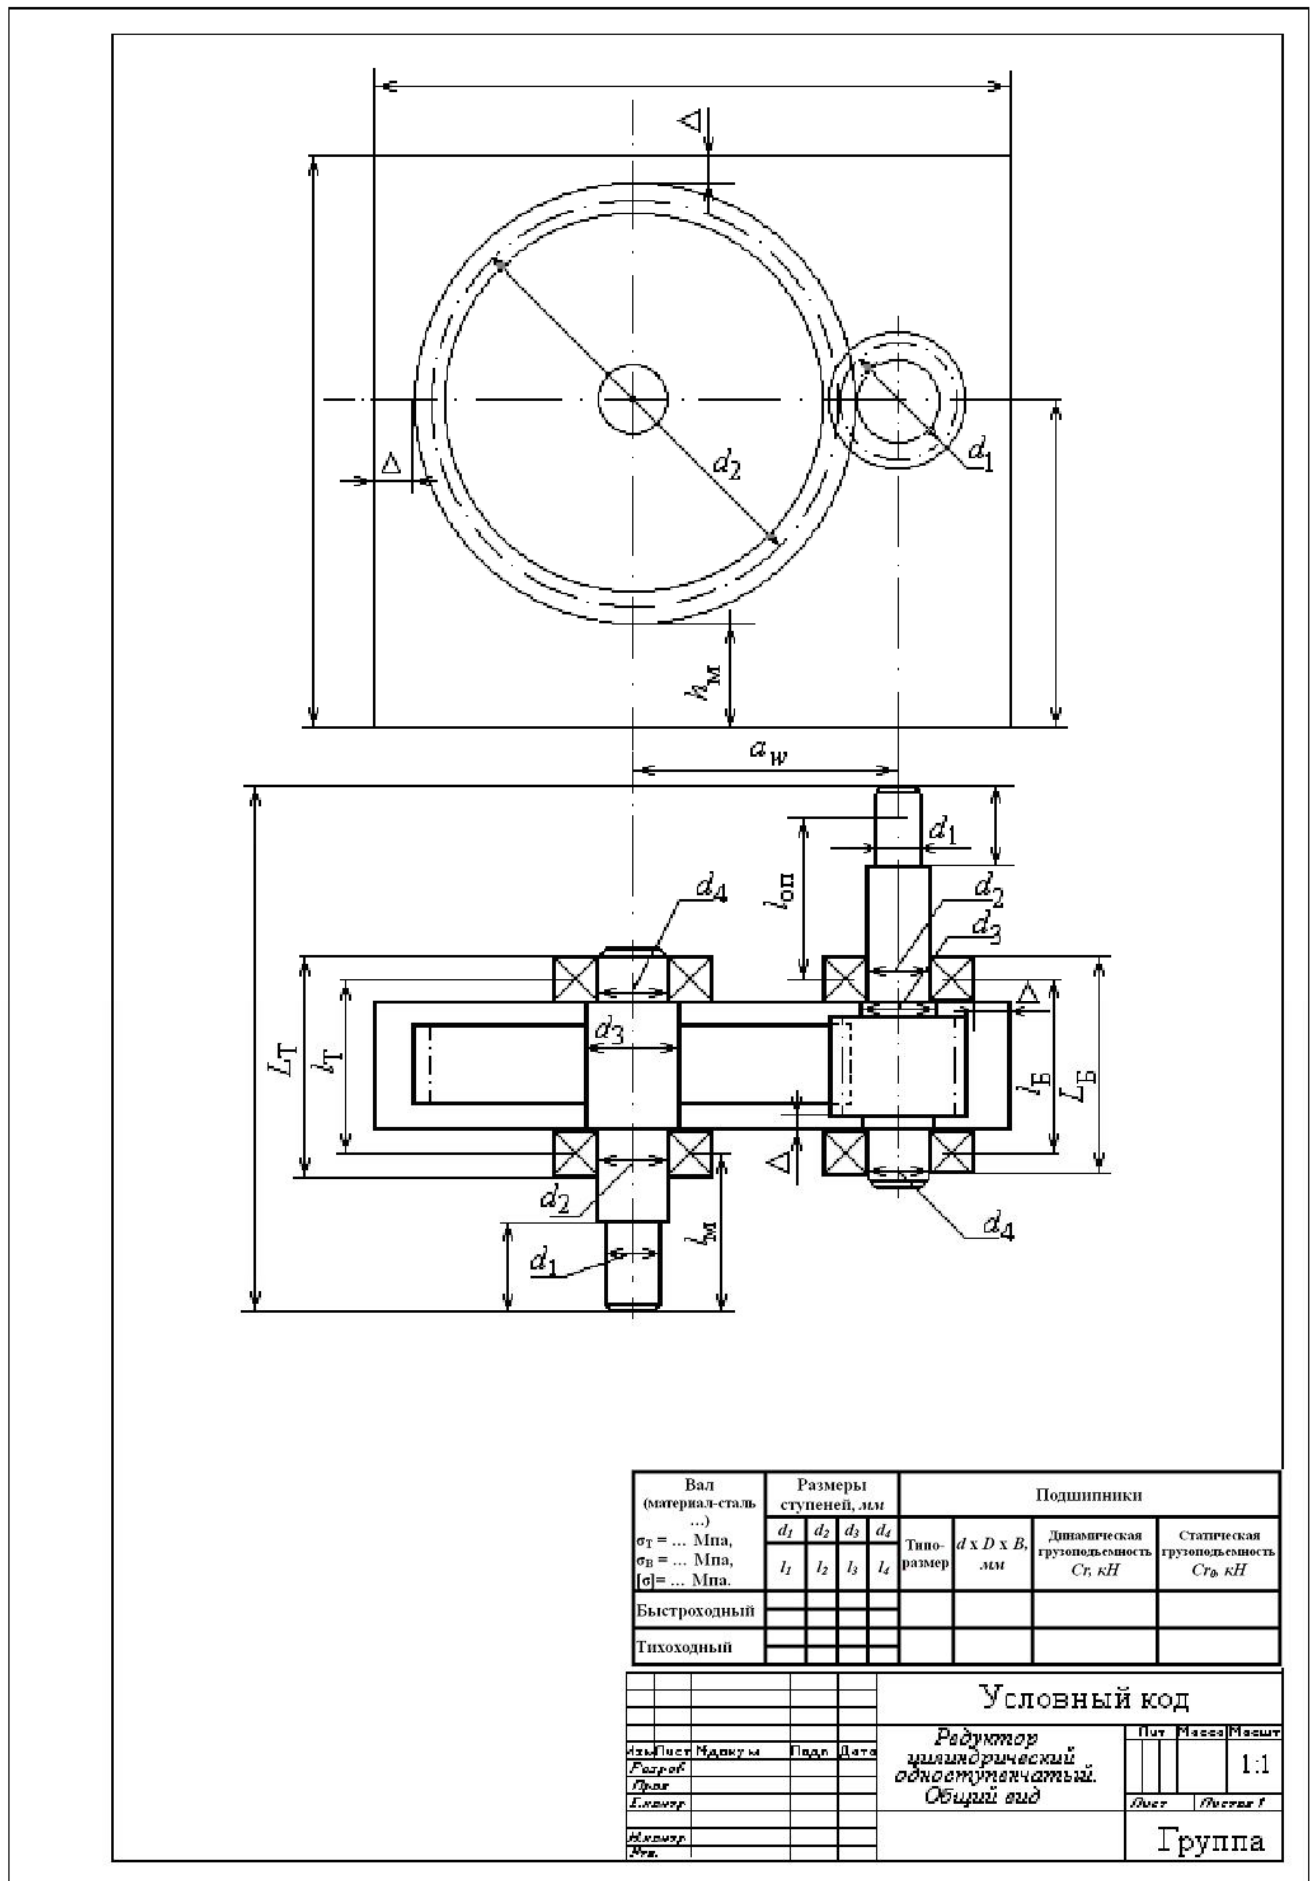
Чертеж общего вида цилиндрического одноступенчатого редуктора
